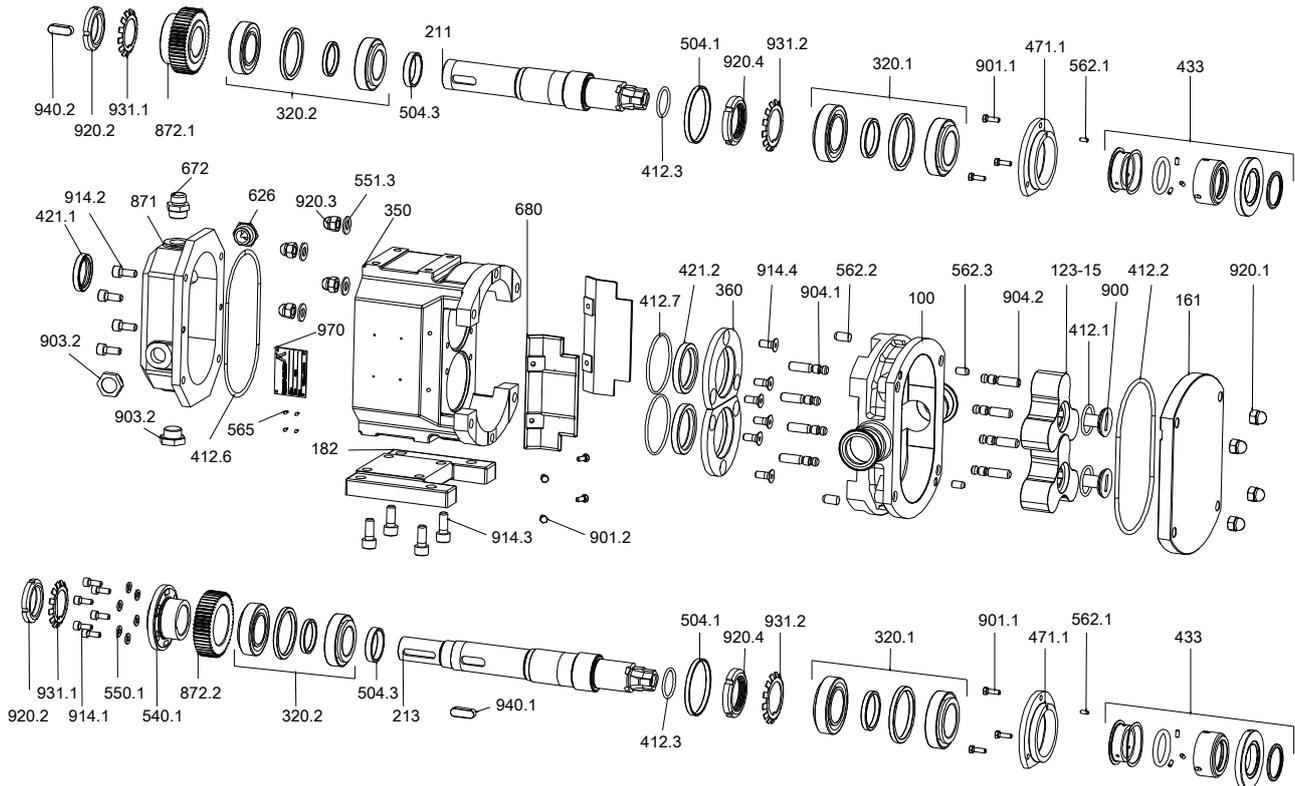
Explosionszeichnung Vitalobe Baugröße 215 bis 490
